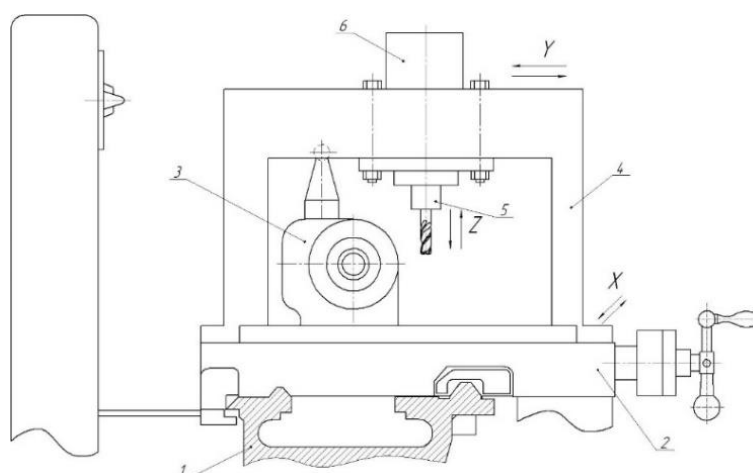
Модернизация токарного станка путем установки фрезерного приспособления на суппорт.
